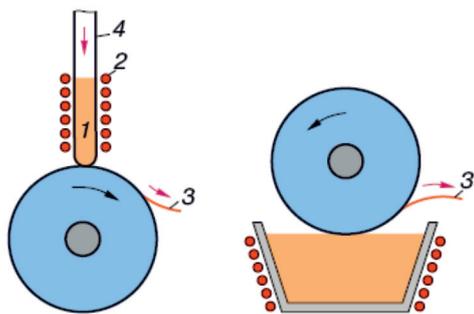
Схемы устройств для получения аморфных сплавов закалкой из жидкого состояния: а – нанесение расплава на вращающийся металлический диск или цилиндр; б – извлечение расплава вращающимся диском; 1 – расплав; 2 – нагревательное устройство (индукционная печь); 3 – лента аморфного сплава; кварцевая трубка
